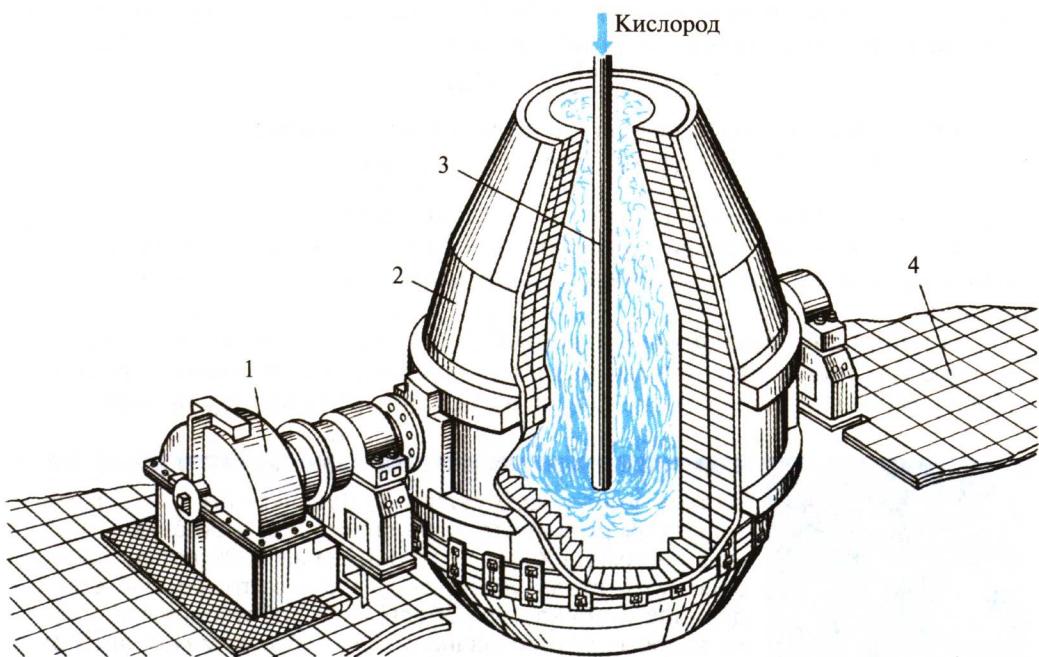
Конвертор: 1 — механизм опрокидывающего устройства; 2 — конвертор; 3 — фурма; 4 — площадка для заливки чугуна
